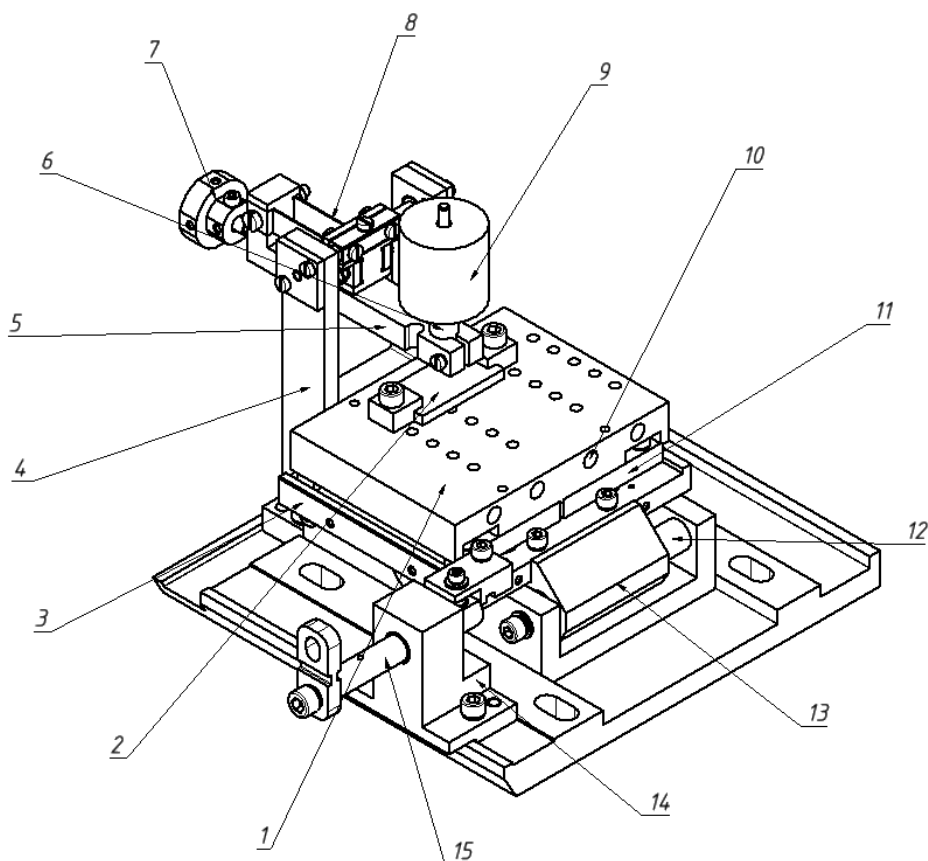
Конструкция трибометрической системы станда. 1 – предметный столик; 2 – исследуемый образец; 3 – подвижная платформа; 4 – измерительная стойка; 5 – балка для крепления контртела; 6 – стержень, 7 – грузы-противовесы, 8 – тензопластины, 9 – груз для создания нормальной силы, 10 – патронные нагреватели, 11 – керамические бруски, 12 – направляющие, 13 – корпус с втулками, 14 – опора штока, 15 – шток.
